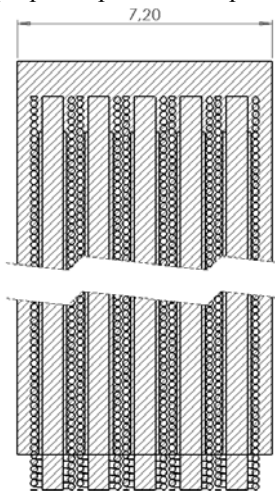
Чертеж нагревателя, вид сверху в разрезе
